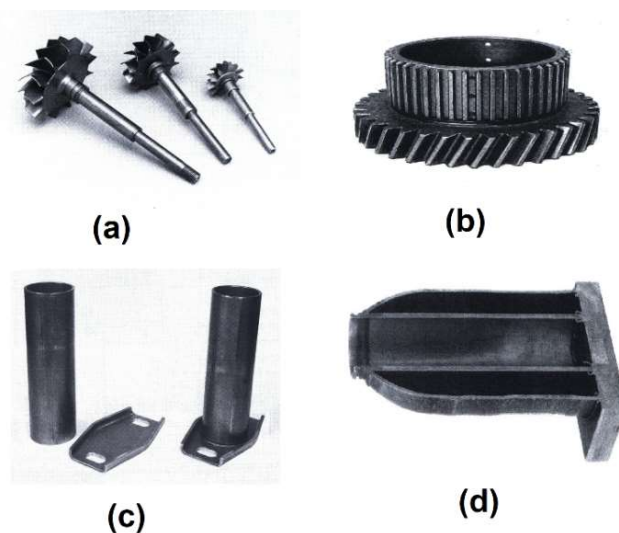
a) Pièce d'un turbo. b) Partie d'une boîte de vitesse. c) Partie d'un amortisseur tube soudé à une pièce comprimée. d) Partie d'un cric hydraulique : le tube à double paroi est soudé en une fois [9].
